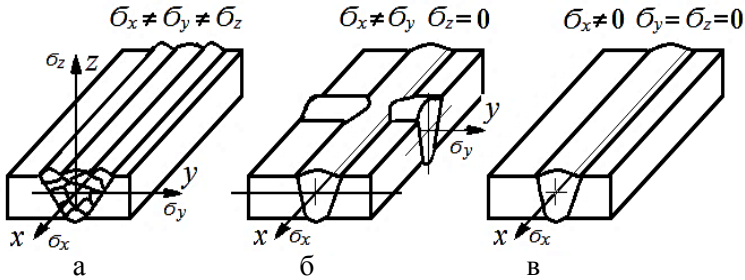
Схема різних видів напруженого стану I роду в зварному з'єднанні: об'ємний або тривісний (а); площинний або двовісний (б); лінійний або одновісний (в)
